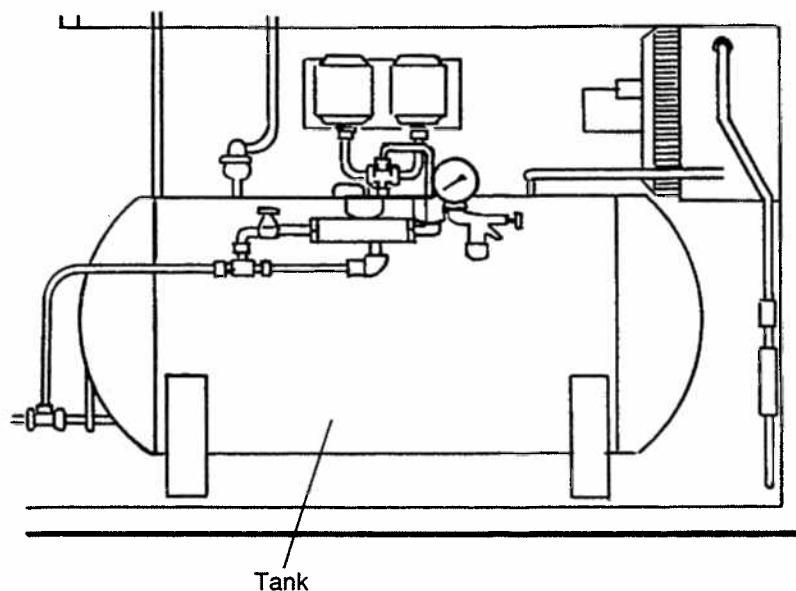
Placering av backventiler F5905-000089 i tryckluftsystemet
